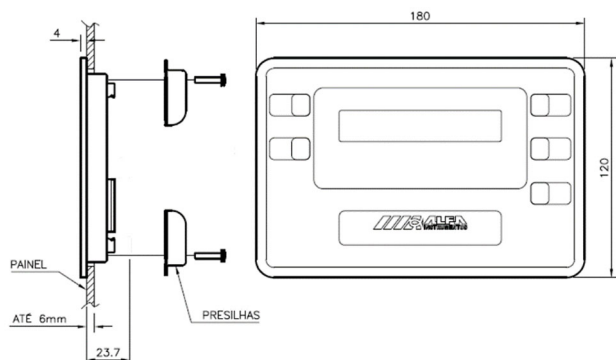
Linha 3100DS dimensões do Indicador de Pesagem
